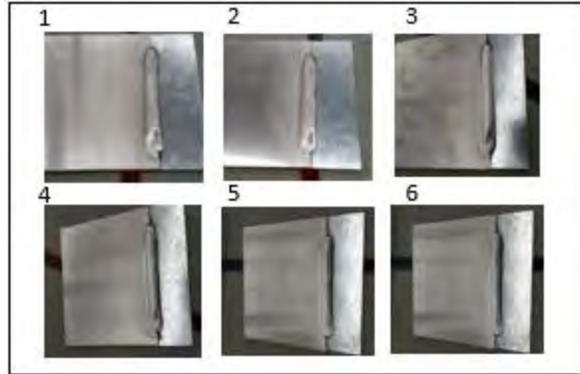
Cordones de soldadura del proceso CMT a un ángulo de 45°
